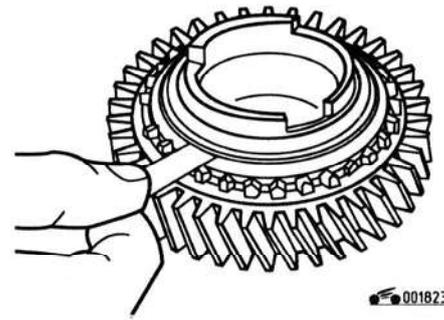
Проверка внутреннего кольца синхронизатора II передачи
